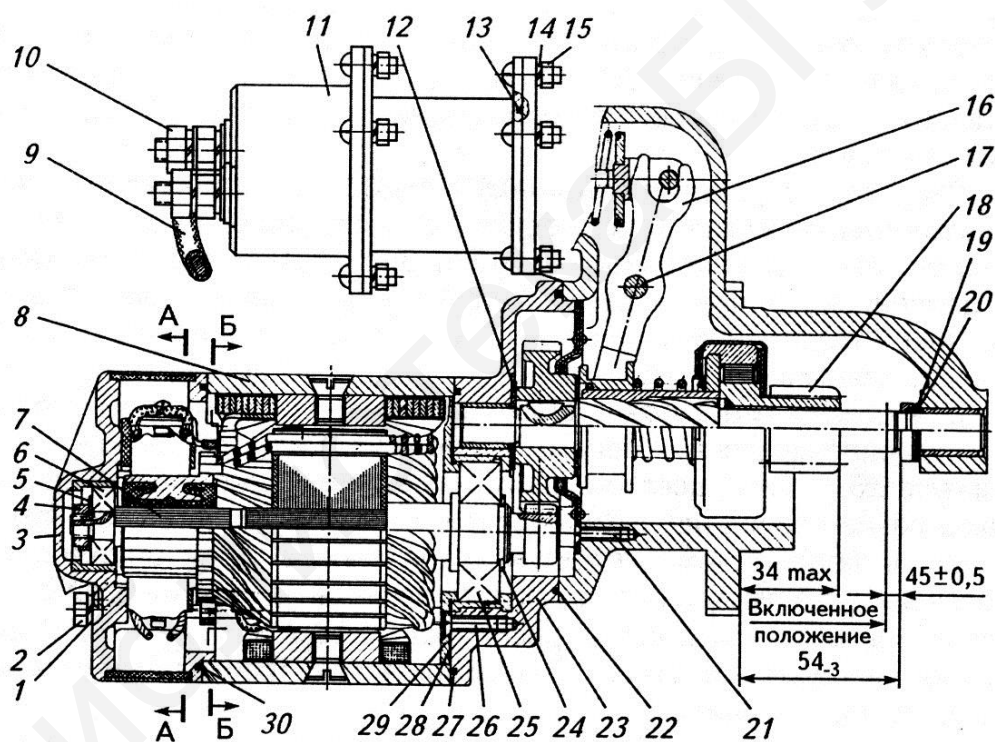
Стартер со встроенным цилиндрическим редуктором с внешним зацеплением:
